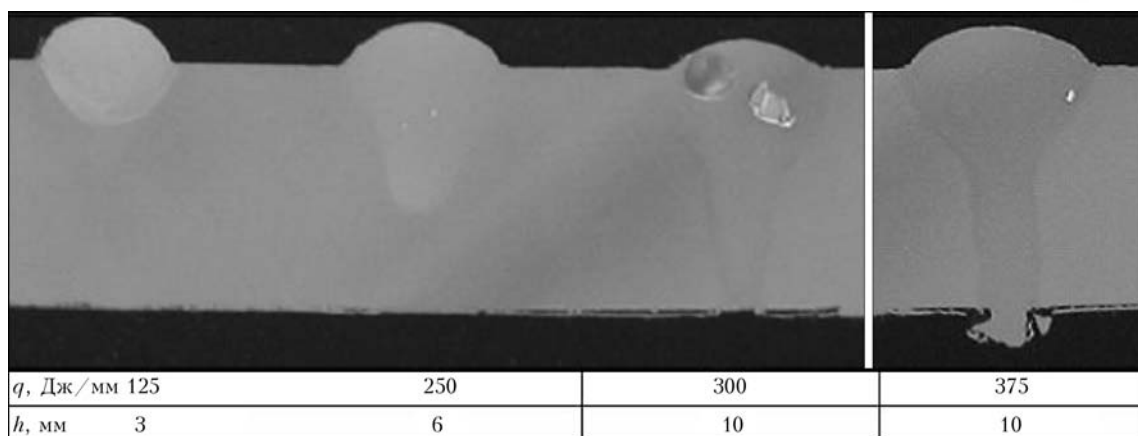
Проплавление пластины сплава АМг6 при применении лазерной сварки с присадочной проволокой с $v_{пл} = 19$ м/мин
